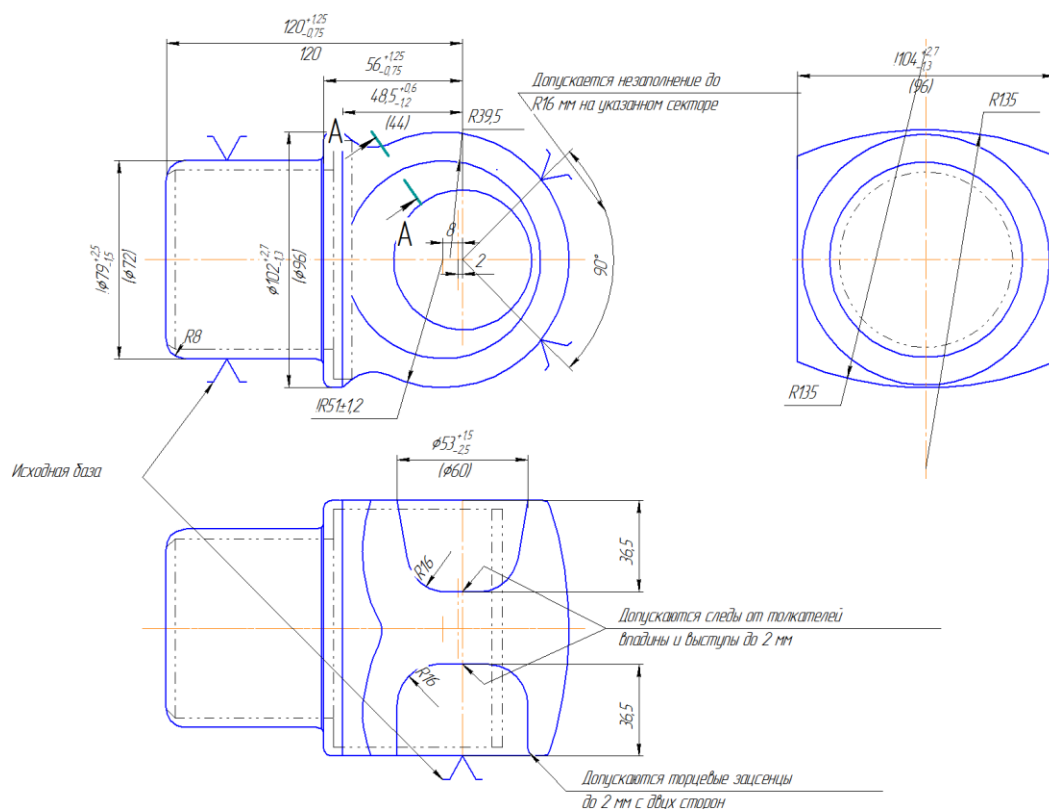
Эскиз заготовки для вилки полуоси
